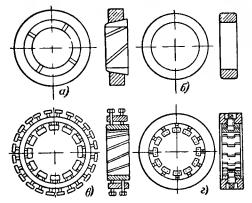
Кольца для прессовки комплекта пластин коллектора.
